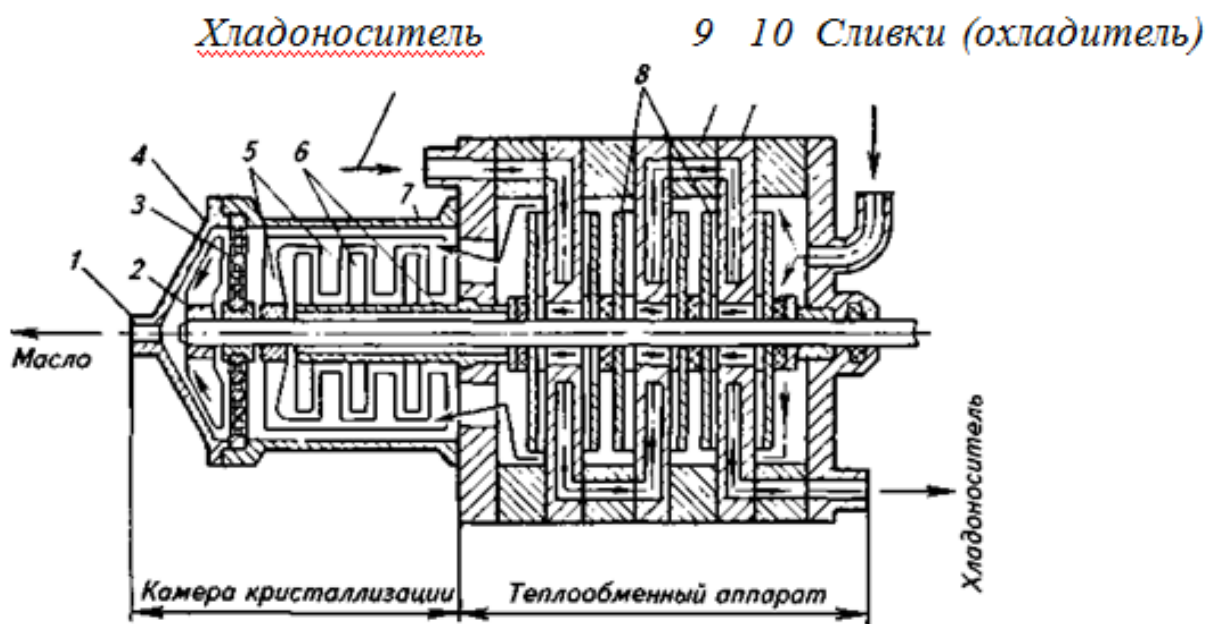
Пластинчатый маслообразователь: 1 – выходной патрубок; 2 – крыльчатка; 3 – дисковые решетки; 4 – конусная насадка; 5 – мешалка; 6 – отражатель; 7 – цилиндр; 8 – диски-турбулизаторы; 9 – продуктовая пластина; 10 – охлаждающая пластина
